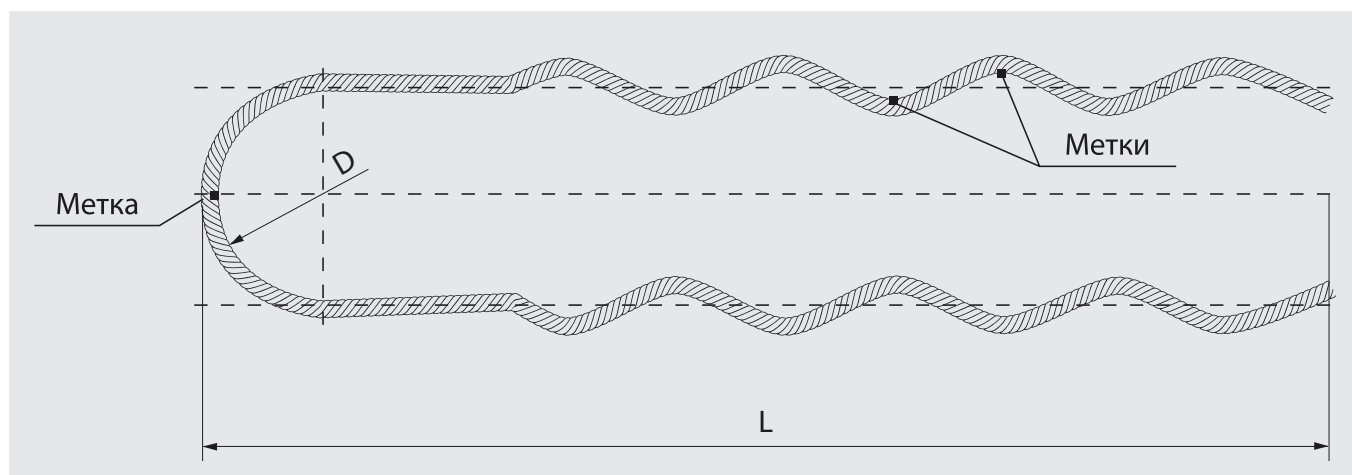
Вязка натяжная для двойного крепления провода.
